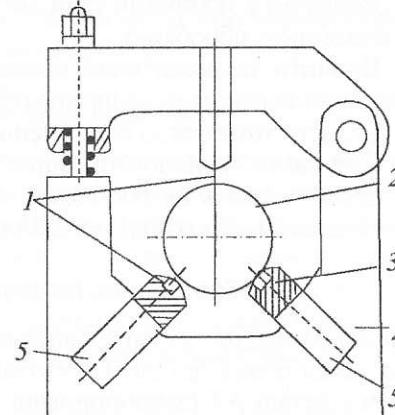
Схема кулькової обкатки зовнішніх циліндричних поверхонь:
